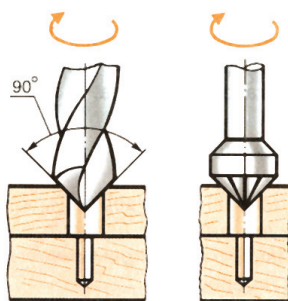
Подготовка гнезда под головку шурупа сверлом
